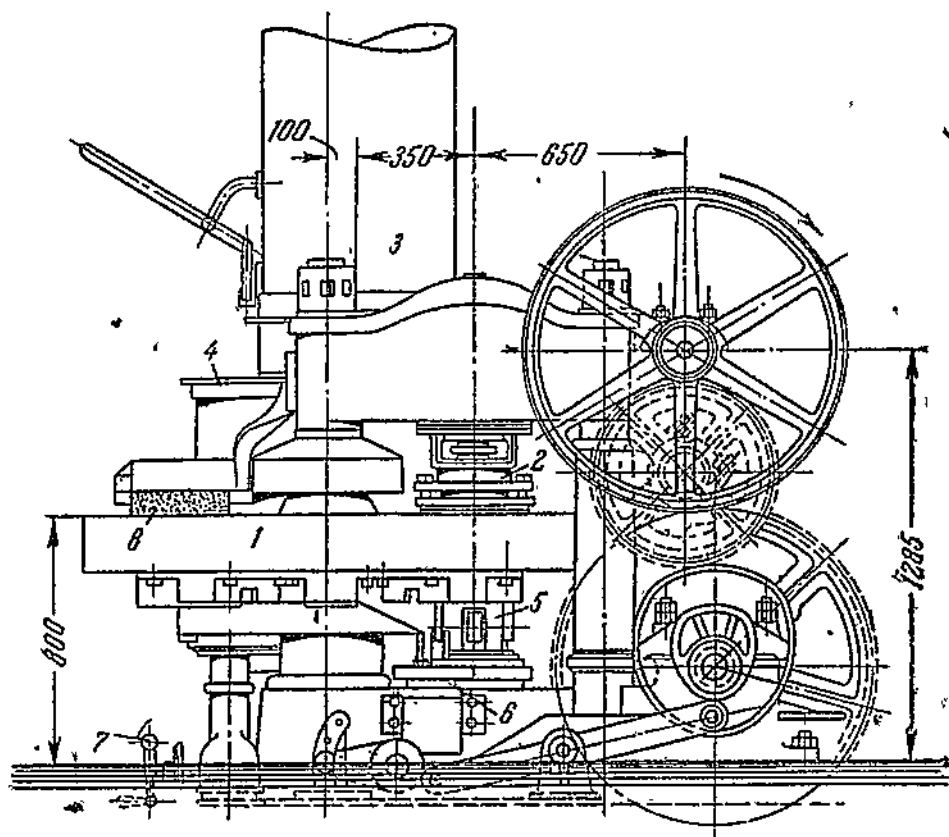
Пресс с поворотным столом системы Бернгарди (вид сбоку):
